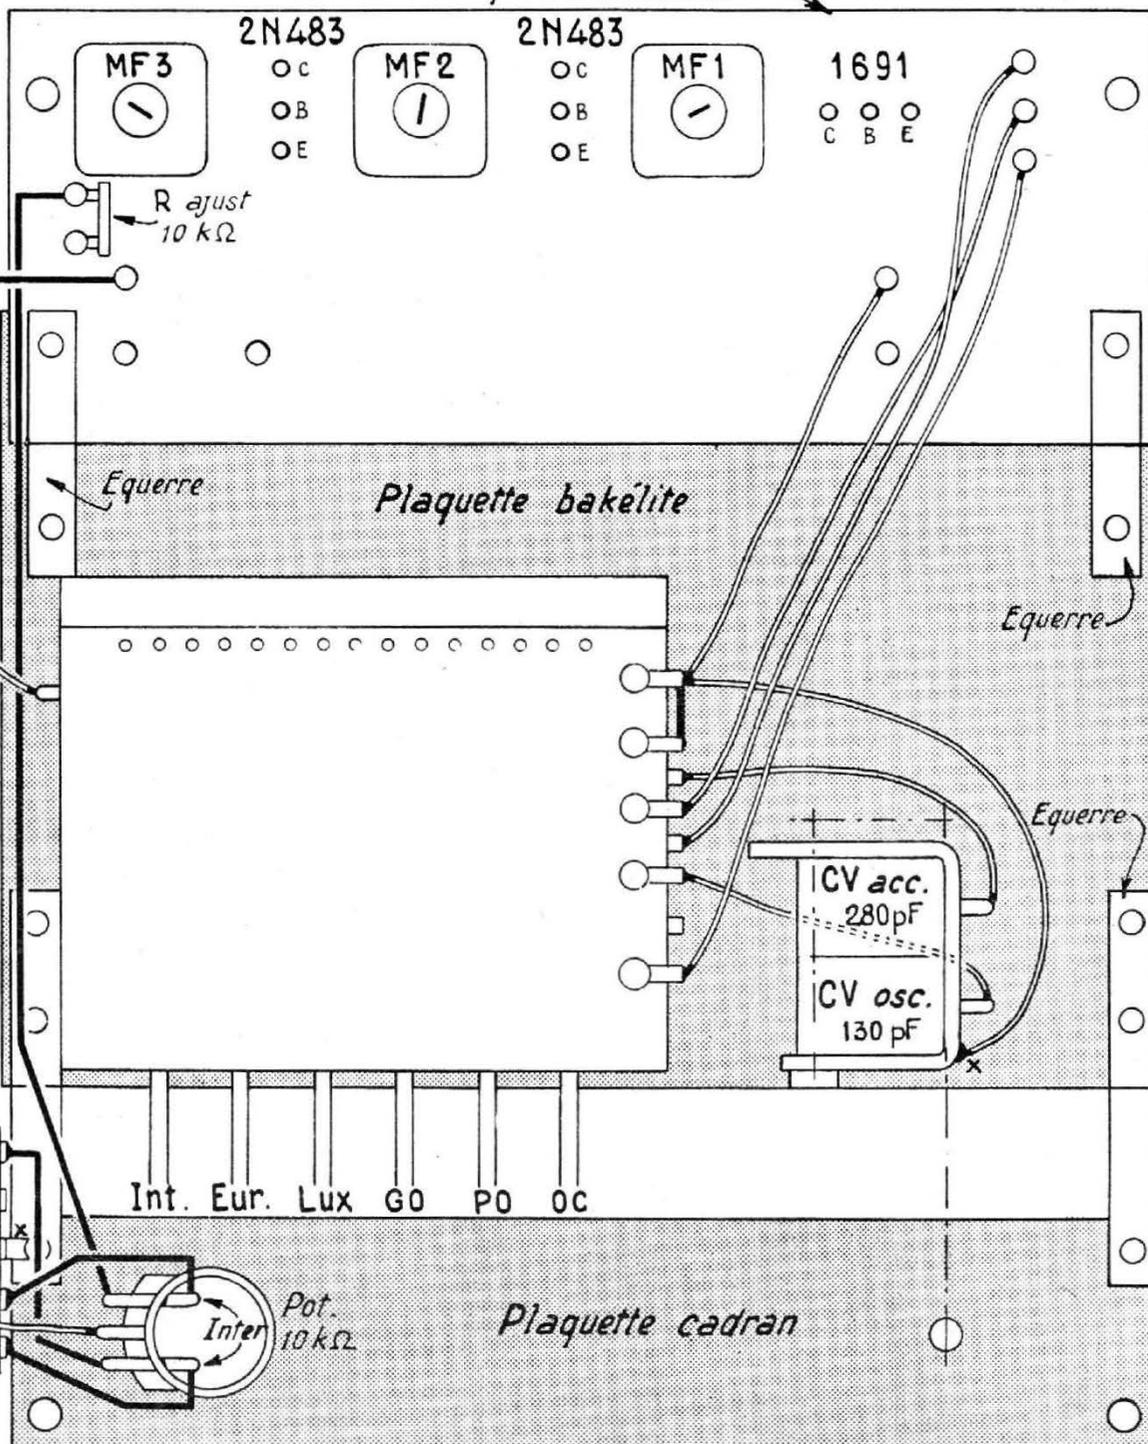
Plan de câblage du boîtier HF du récepteur
